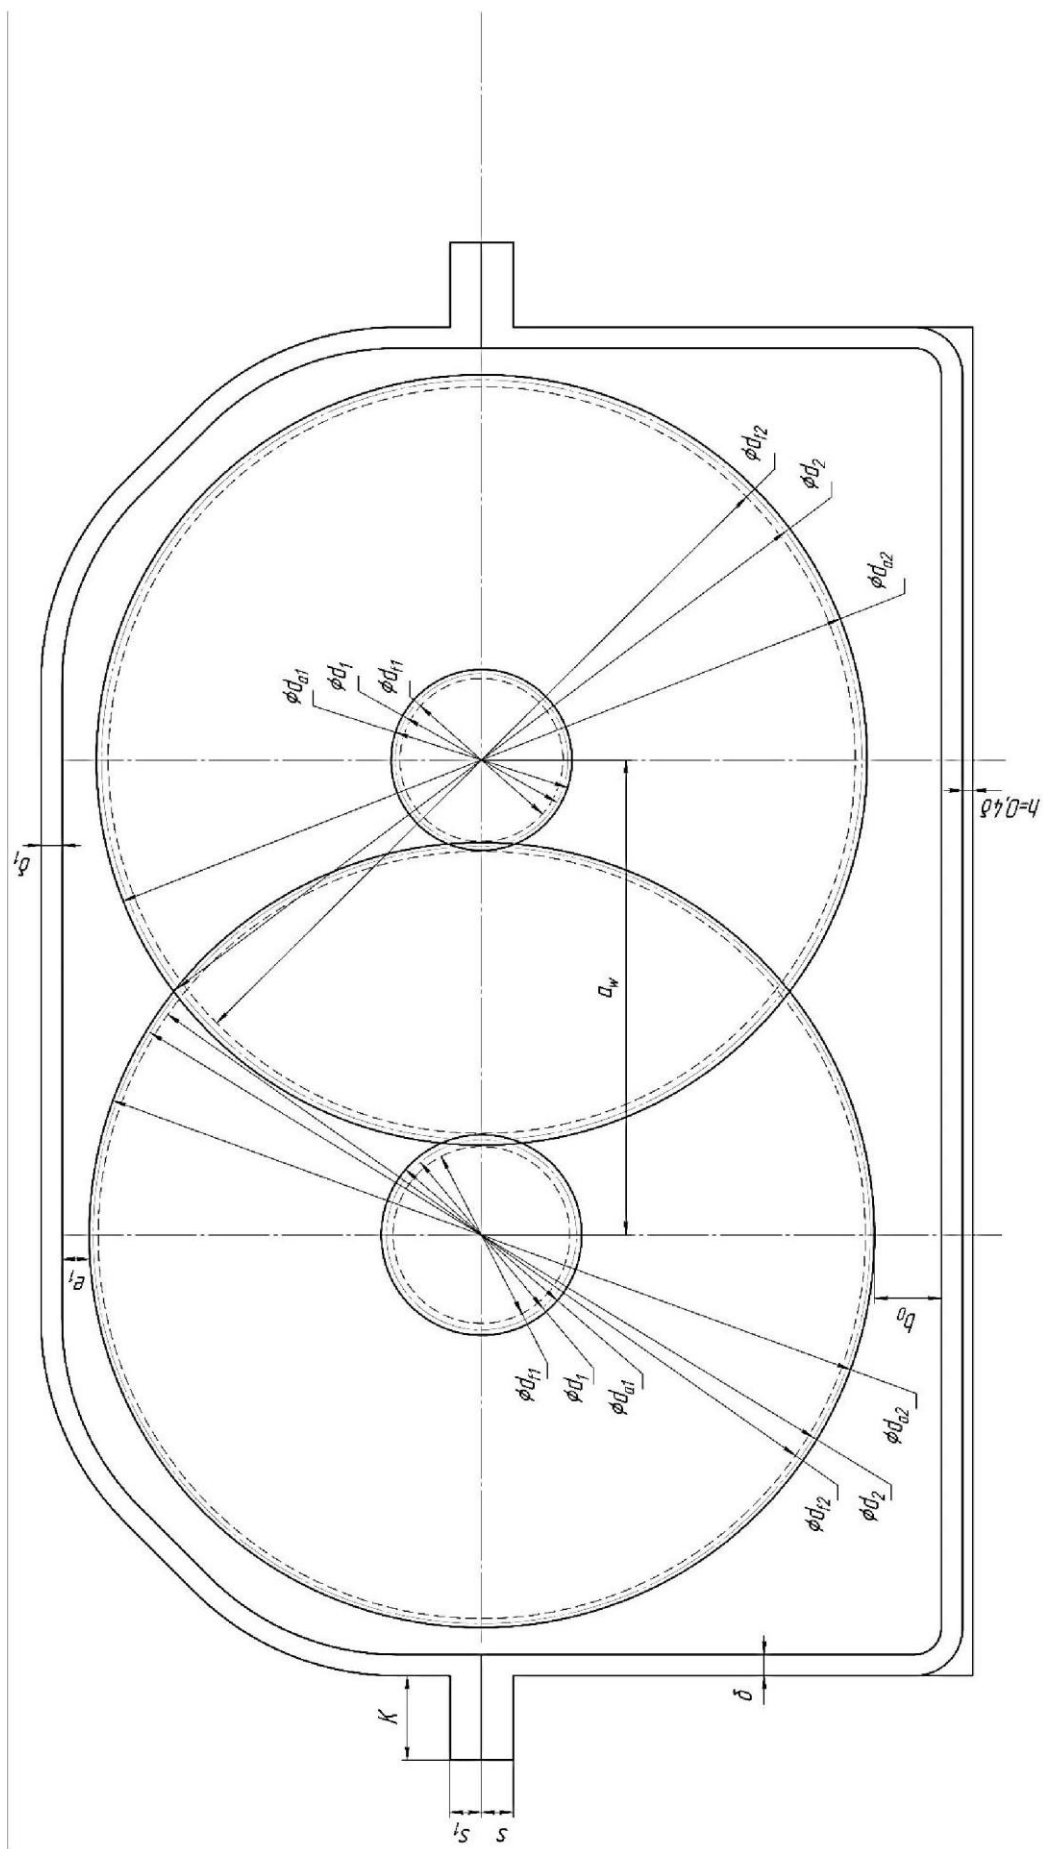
Компонувальне креслення співвісного циліндричного редуктора (початок)
